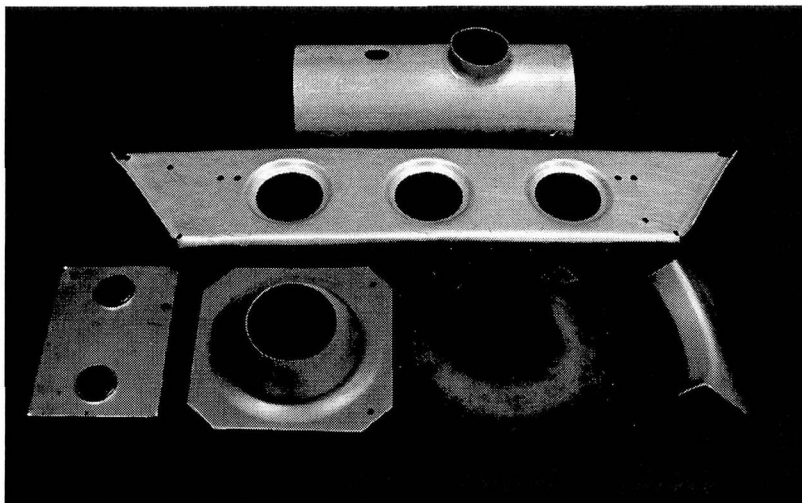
Типовые детали летательного аппарата, изготовленные отбортовкой
